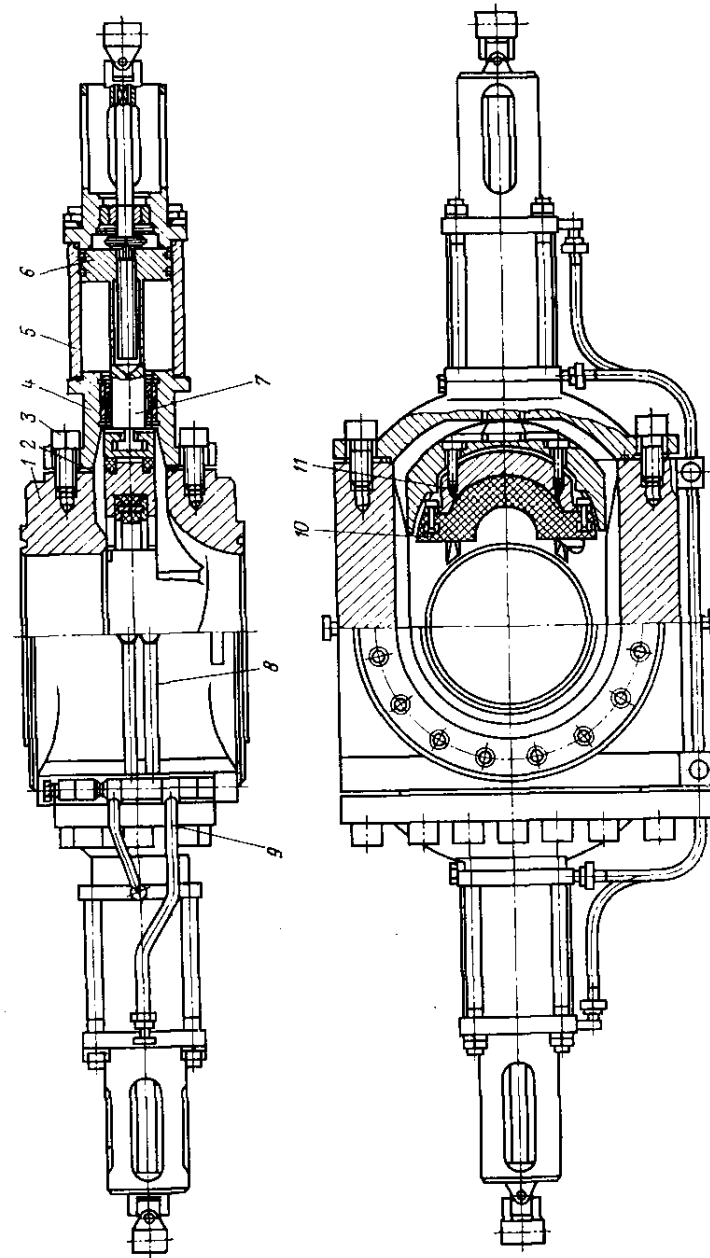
Превентор плашечный: 1 — корпус; 2 — резиновые прокладки; 3 — винты; 4 — откидные крышки; 5 — гидравлический цилиндр; 6 — поршень; 7 — шток; 8 — коллектор; 9 — трубопровод; 10 — резиновые уплотнения; 11 — сменные вкладыши
